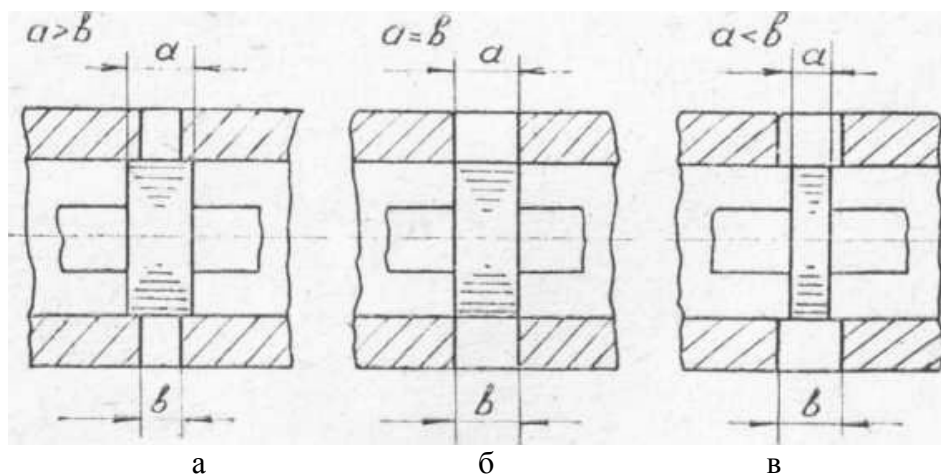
Схемы перекрытия цилиндрических золотников: а – с положительным перекрытием, б – с нулевым перекрытием, в – с отрицательным перекрытием
